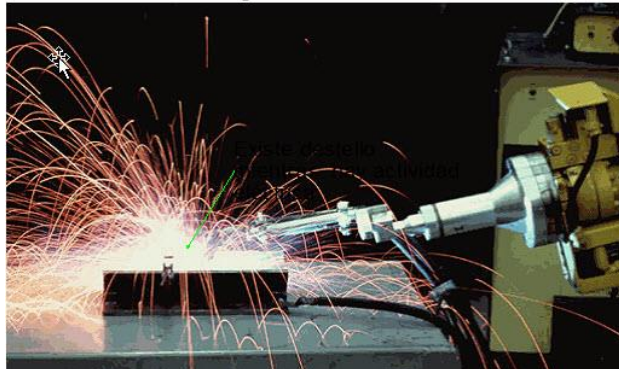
Efecto de la soldadura eléctrica con el oxígeno
